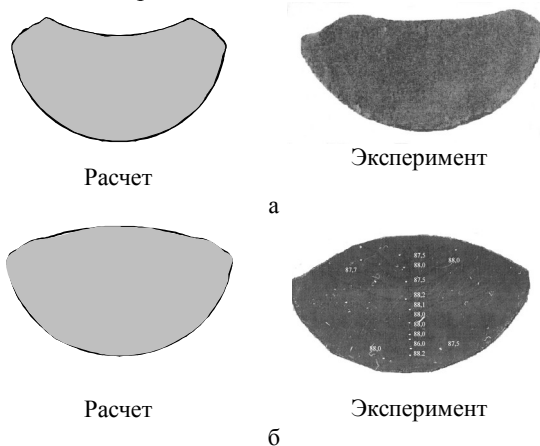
Форма заготовки при радиальном прессовании сегментного цилиндра (а) и круглого цилиндра ступенчатым пуансоном (б)
